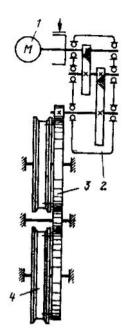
Кинематическая схема механизма передвижения крана на рельсовом ходу: 1 – электродвигатель; 2 – двухступенчатый редуктор; 3 – открытая зубчатая передача; 4 – ходовое колесо
